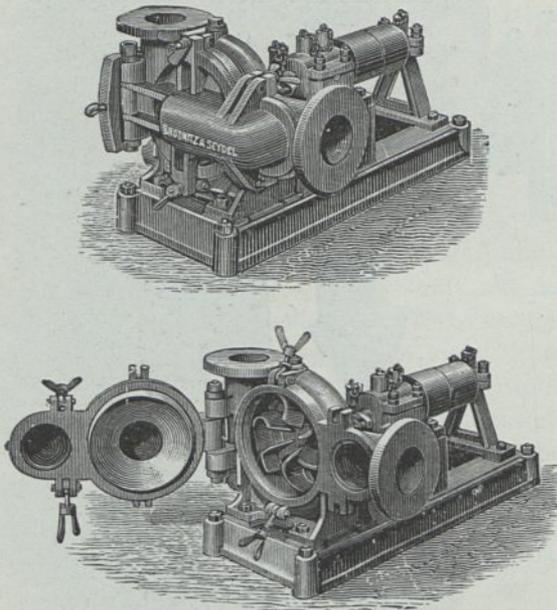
a, b. Zentrifugalpumpe mit Klappdeckel zum Öffnen.
